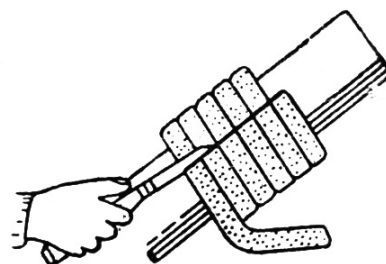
Подготовка набивки к установке в камеру сальника
